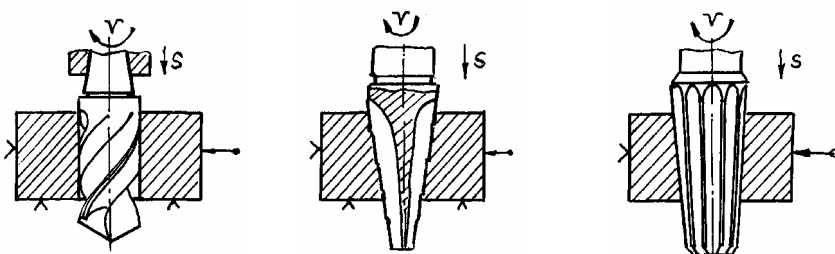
Схема обработки отверстий и применяемый режущий инструмент
